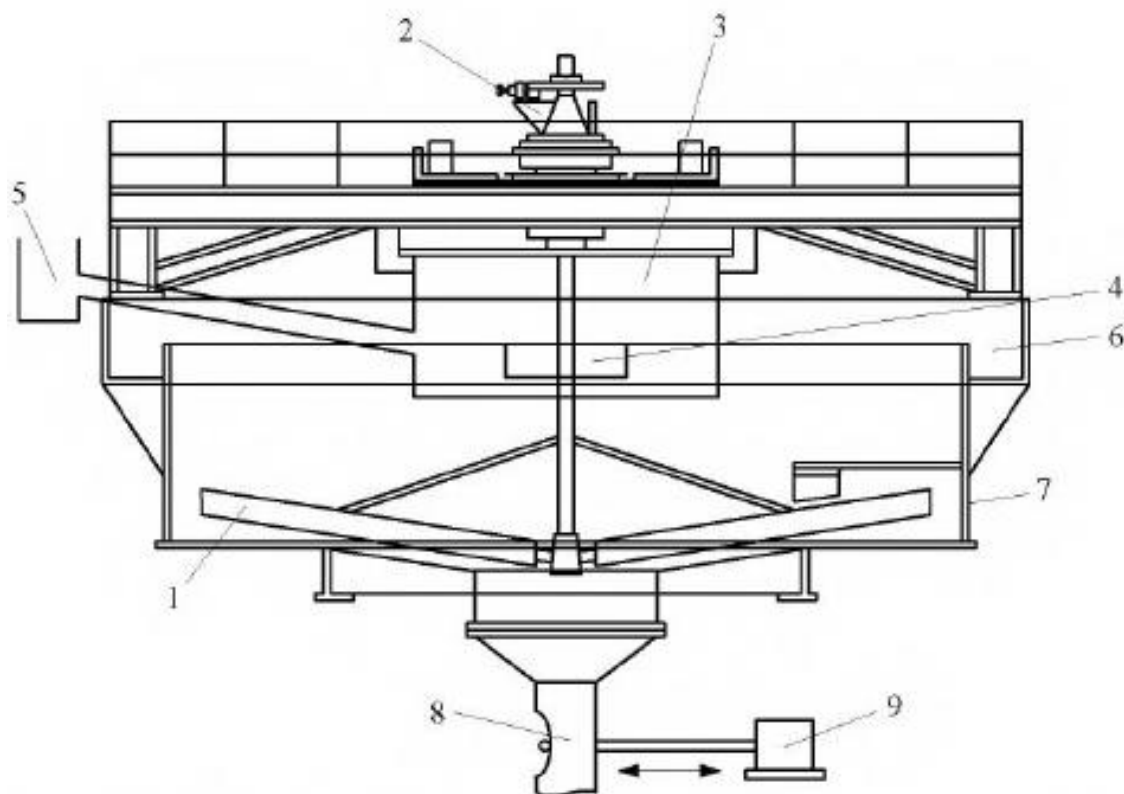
Загальний вид магнітного дешламатора МД:
